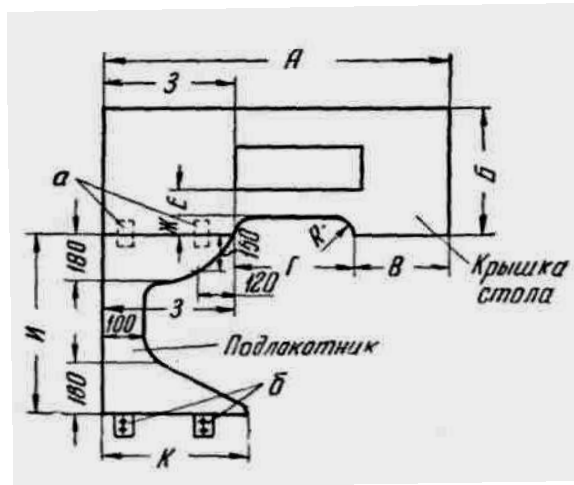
Крышка стола с подлокотником: а — навески; б — планки металлические
